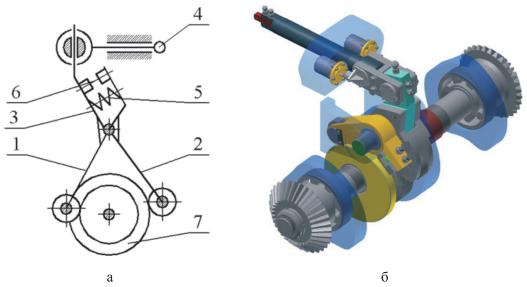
Механизм отрезки холодноштамповочного автомата AB1818: а — кинематическая схема; б — твердотельная модель; 1 — рычаг прямого хода; 2 — рычаг обратного хода; 3 — рычаг; 4 — исполнительное звено; 5 — пружина; 6 — регулируемый зазор; 7 — блок кулаков
